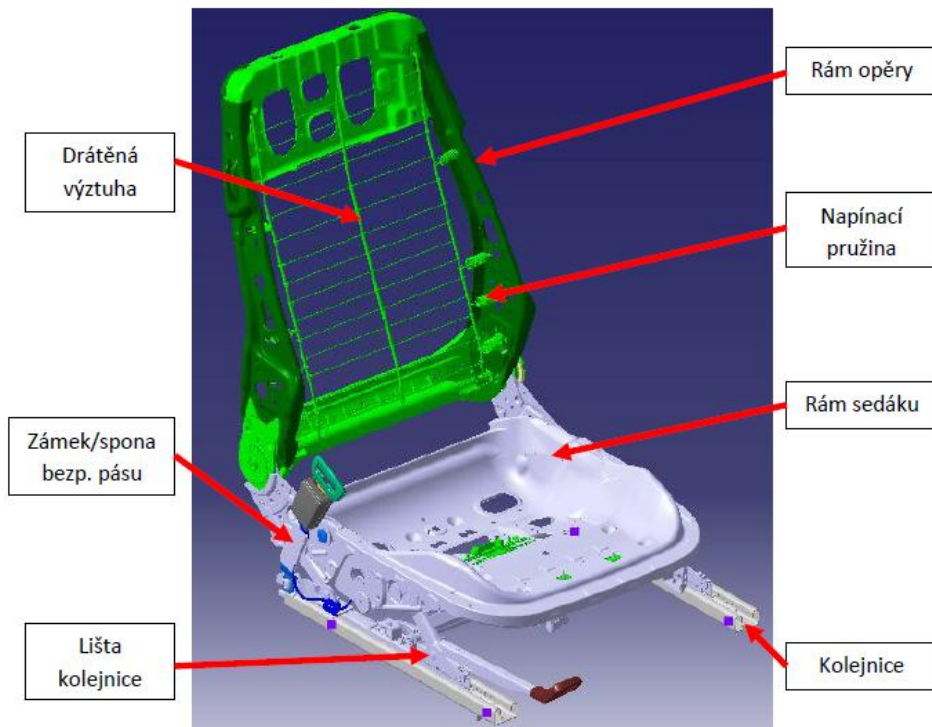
Moderní sedadla vozu BMW M3 [5]
